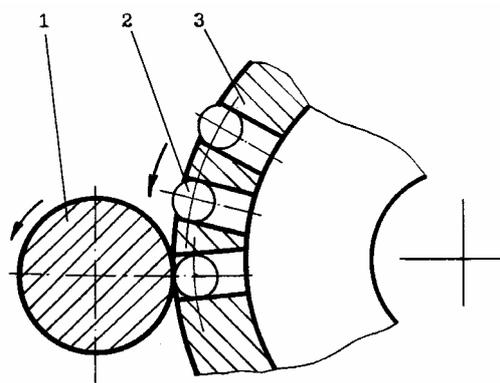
Схема устройства для ротационного упрочнения: 1 – деталь; 2 – шарики; 3 – корпус
